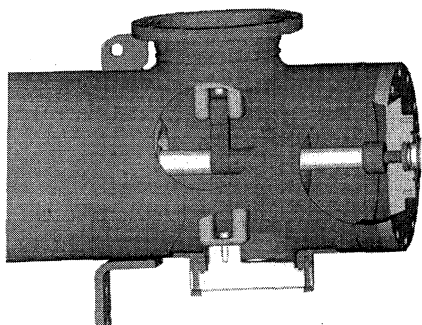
Комбинированный разъединитель-заземлитель ячейки PASS MO с одной системой шин (подвижный контакт подключен к сборной шине)
